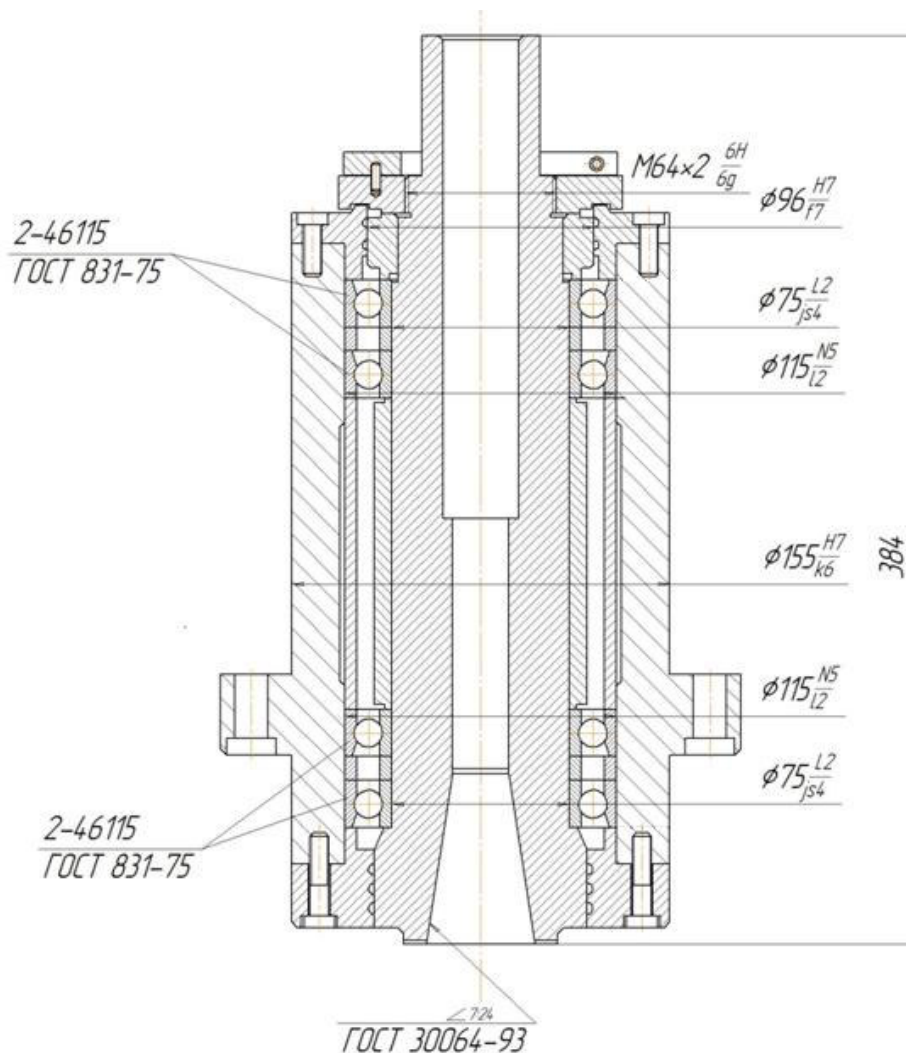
Шпиндельный узел координатно-расточного станка мод. 2440СФ4
